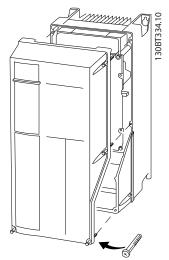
Accès au câblage des protections IP55 et IP66
